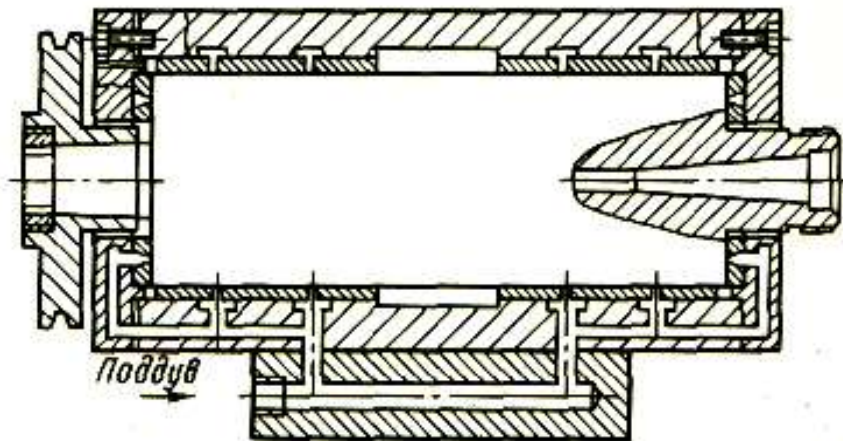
Шпиндельний вузол шліфувального верстата
